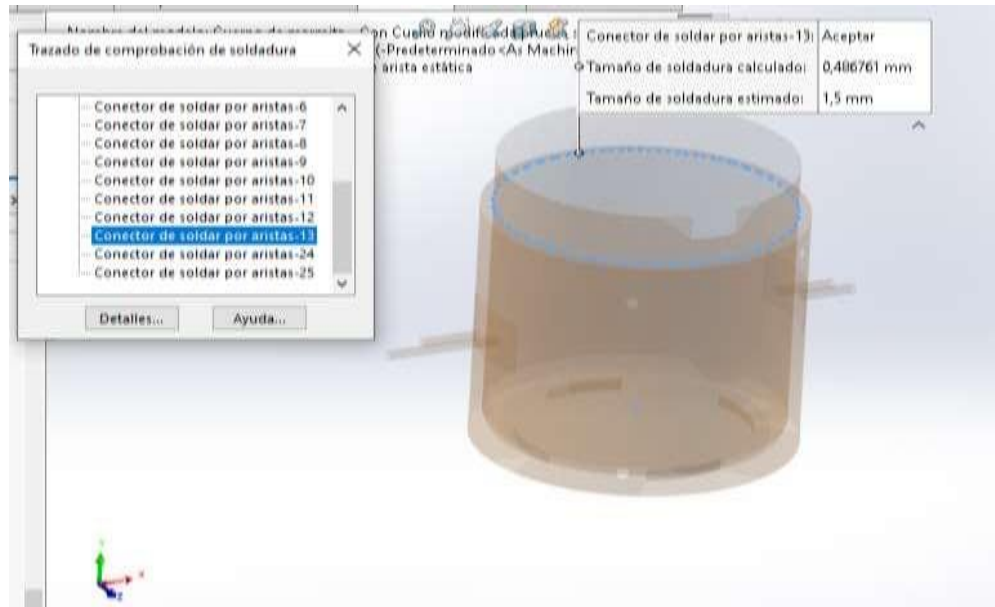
Análisis de cordón de soldadura en punto crítico de la olla. Autoría propia.
